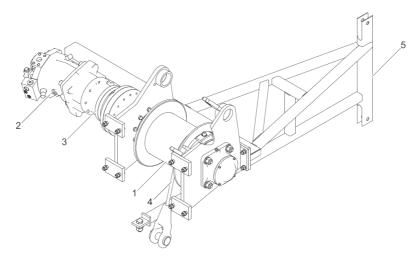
Главная лебедка: 1 – барабан лебедки; 2 – гидравлический двигатель; 3 – редуктор и тормоза в сборе; 4 – стальной трос; 5 – рама шкивов
